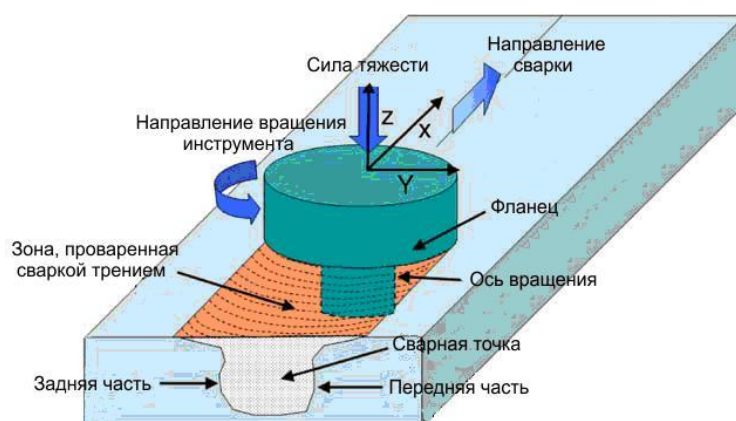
Схема сварки трением с перемешиванием
